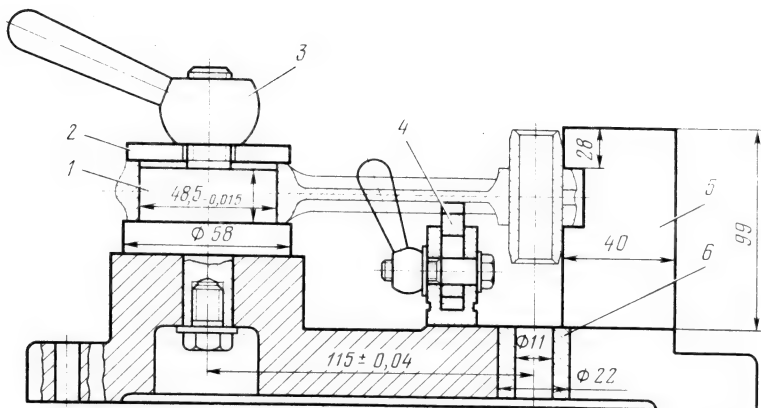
Приспособление для контроля и рихтовки шатунов:
